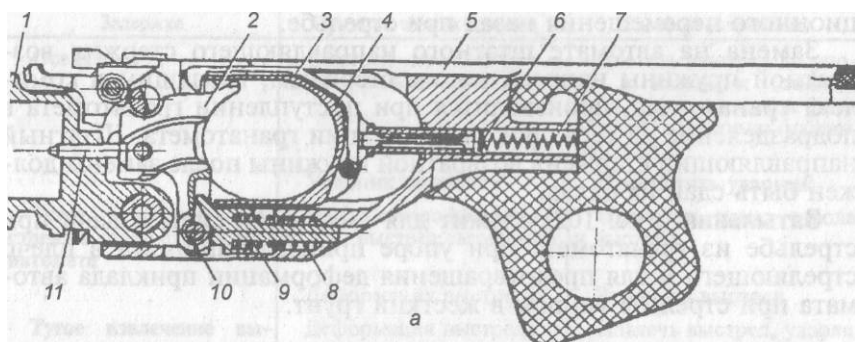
Корпус ударно-спускового механизма с рукояткой:
